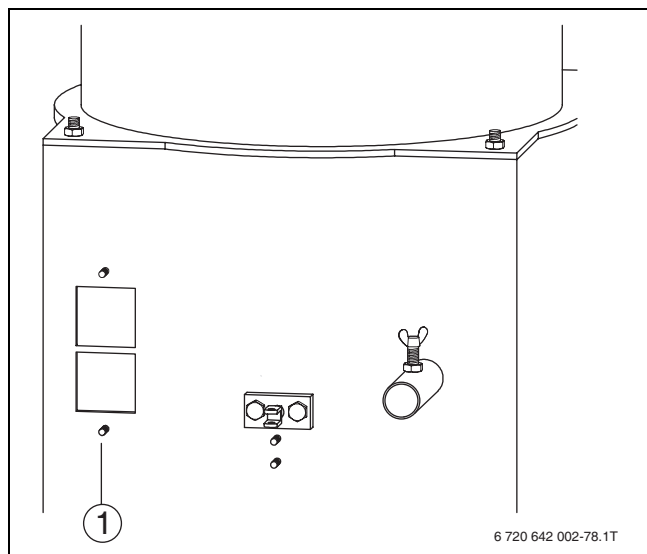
Kontrola snadného chodu motoru čištění hořáku
